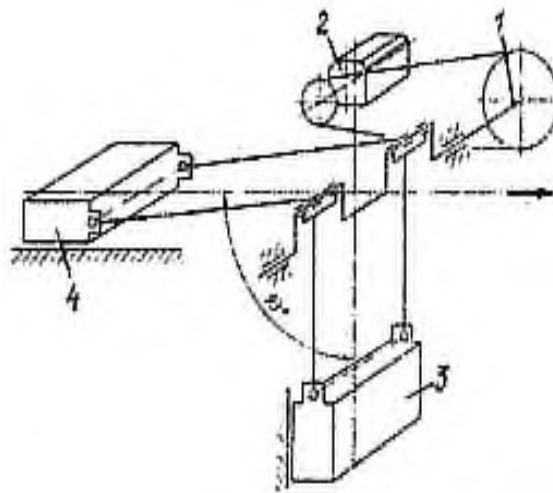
Кинематическая схема приводного механизма стана ХПТ [1]
